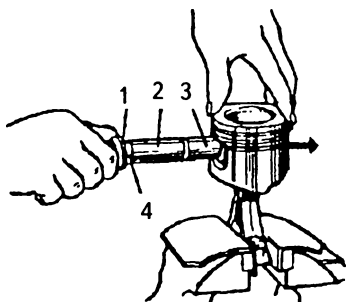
Запрессовка поршневого пальца двигателей ВАЗ в верхнюю головку шатуна с помощью оправки:
